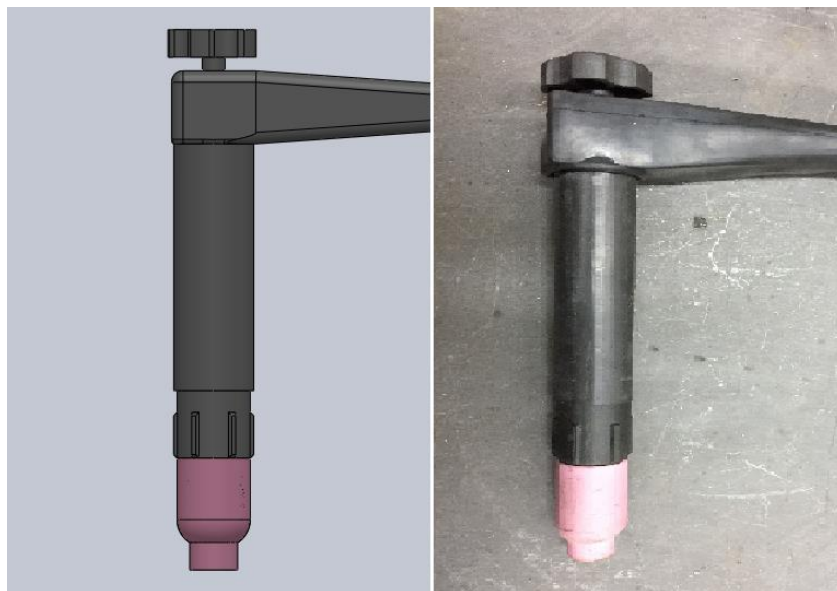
(a) Modelo 3D de tocha de soldagem TIG AUT 27B - 9". (b) Tocha de soldagem comercial TIG AUT 27B - 9".
